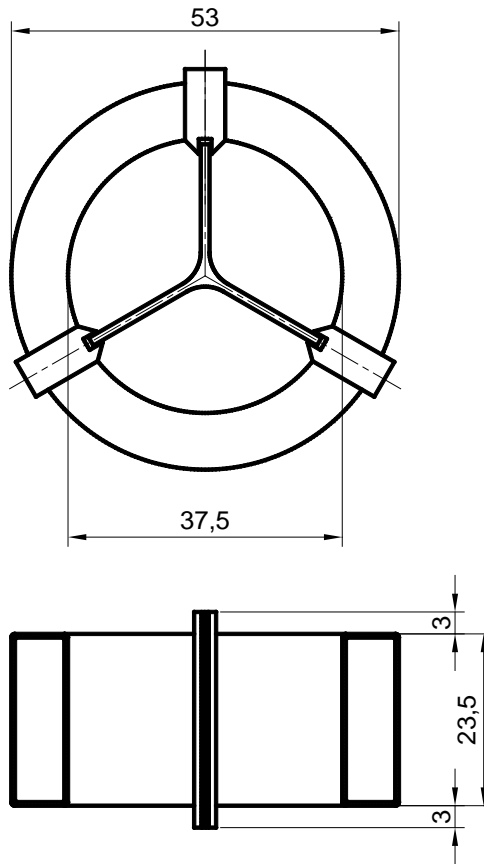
Внешний вид и габаритные размеры магнитопровода MSFN-50S-TH1
